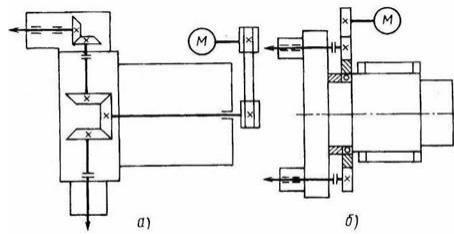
Револьверные головки токарных модулей с вращающимся инструментом:
